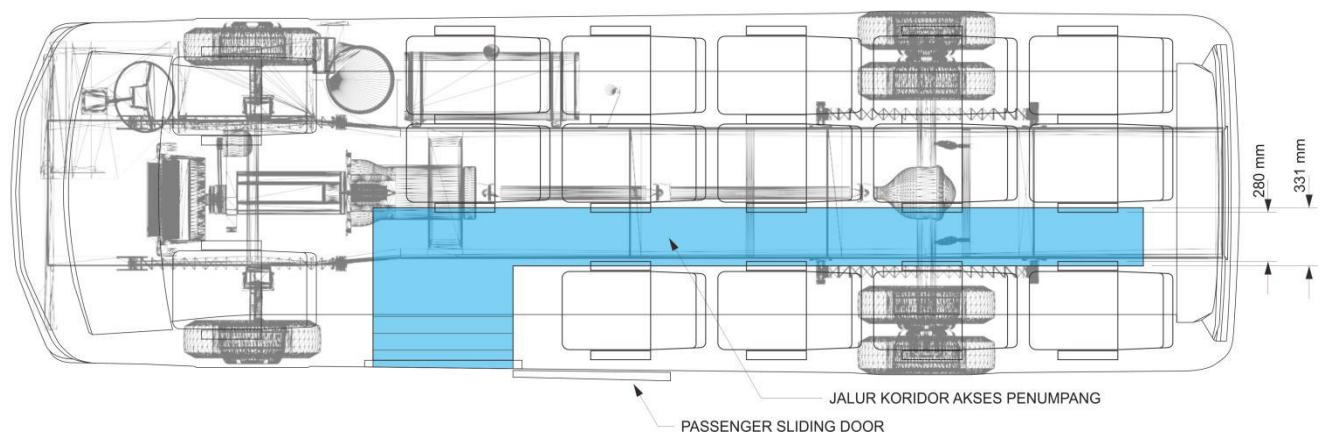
Konfigurasi Passenger Seat Tampak Samping
